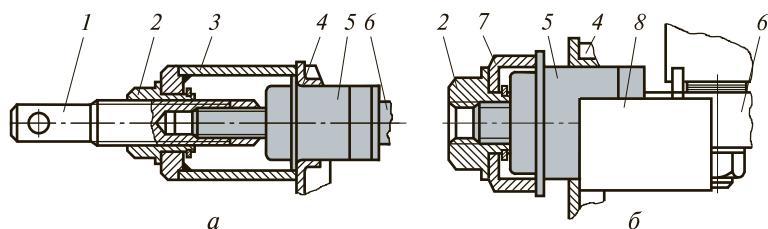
Схемы выпрессовки (а) и запрессовки (б) шарнира нижнего рычага:
